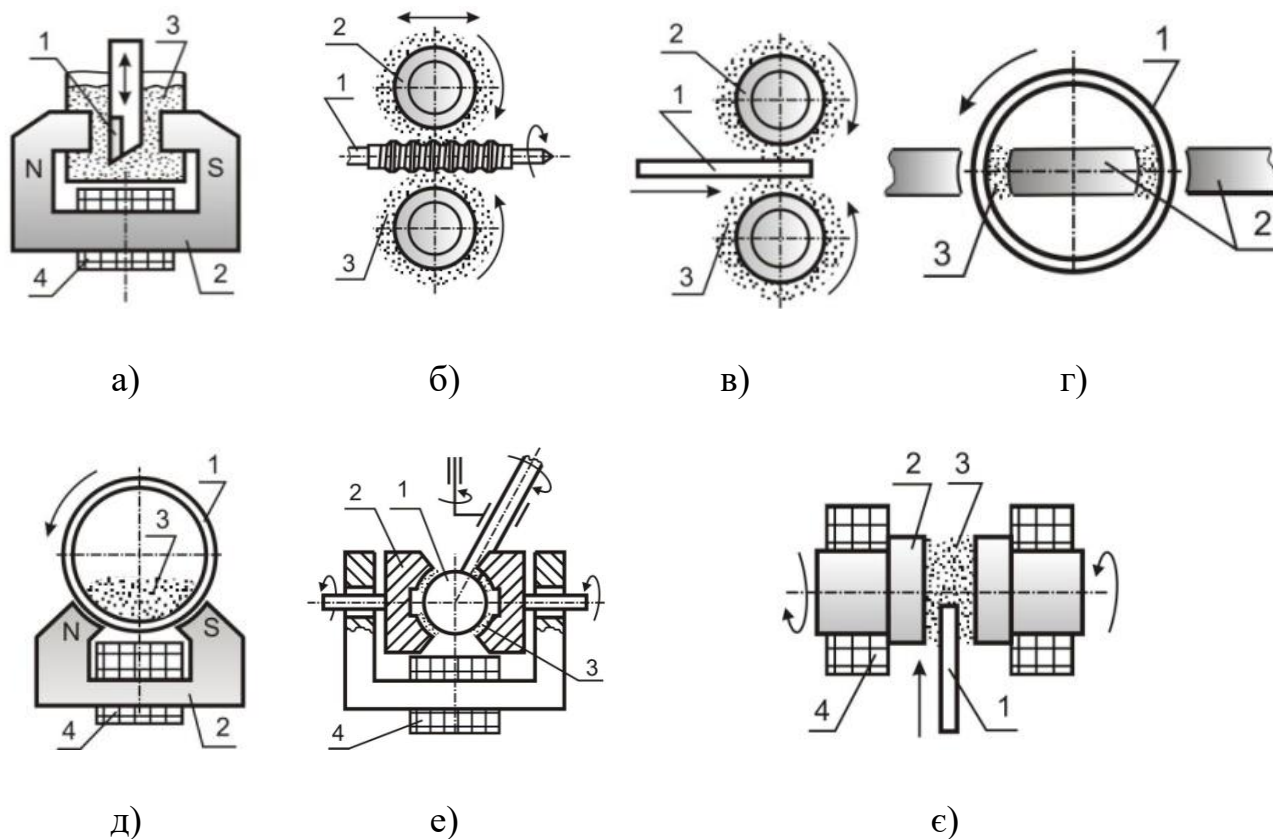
Схеми для МАО а) різальних кромок; б) зовнішньої різьби; в) листового матеріалу; г) внутрішніх поверхонь; д) внутрішніх поверхонь тонкостінних деталей; е) зовнішніх сферичних поверхонь; є) граней деталей: 1- деталь, що обробляється; 2-електромагнітний індуктор змінного струму; 3- камера з порошком; 4-магнітна котушка.
